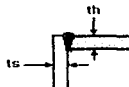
Esquema de soldadura a tope con factor $C=0.33$
